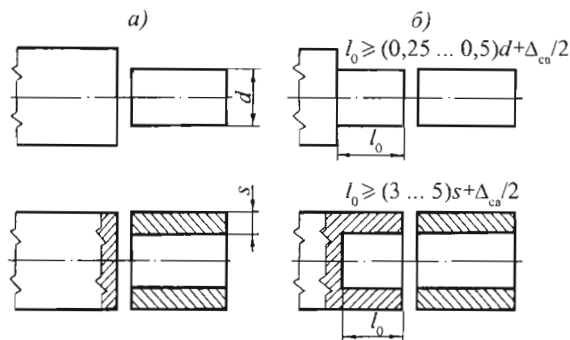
Формы нерациональной (а) и рациональной (б) подготовки торцов деталей к стыковой сварке:  $d$  и  $s$  – диаметр прутка и толщина стенки трубы;  $\Delta_{св}$  – суммарное упрочнение деталей при сварке за счет осадки или оплавления и осадки
